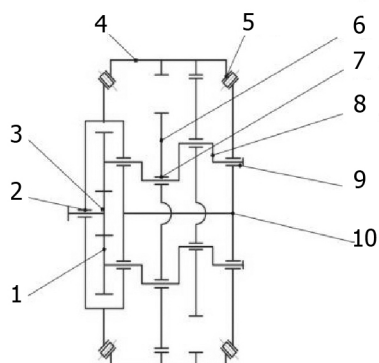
Кинематическая схема планетарного редуктора 2K-V с внецентроидным внутренним цевочным зацеплением: 1 – колесо зубчатое эвольвентной ступени; 2 – опорный подшипник ведущего вала-шестерни; 3 – ведущий вал-шестерня; 4 – корпус редуктора; 5 – совмещенные конические опоры качения водила; 6 – эпициклоидный сателлит; 7 – опорные подшипники эпициклоидных сателлитов; 8 – вал эксцентриковый; 9 – опорные подшипники эксцентриковых валов; 10 – водило
